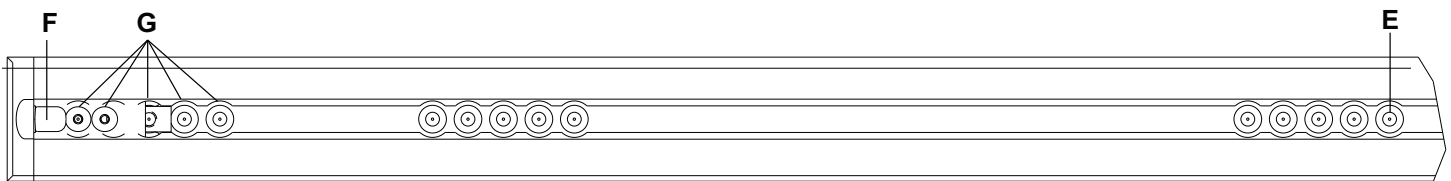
Posizione localizzatore piastra a pavimento - lato piedi
